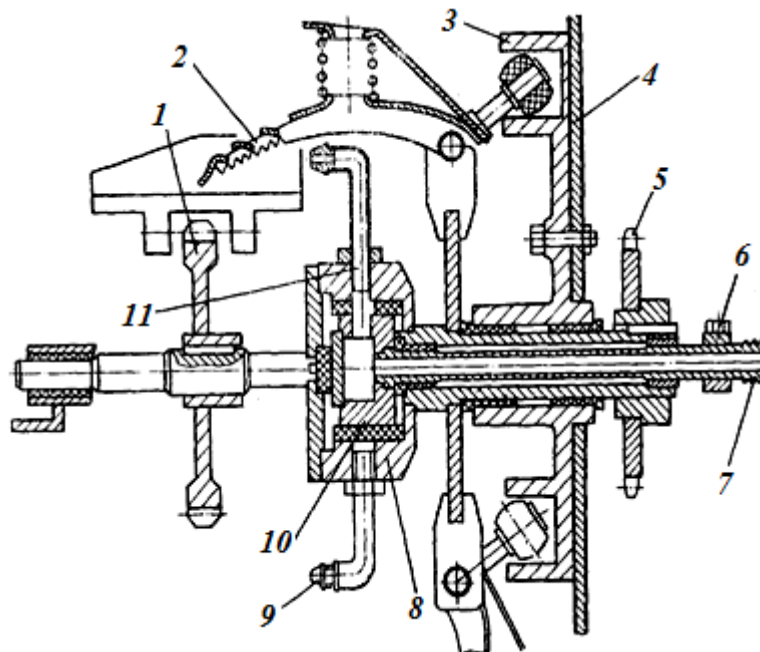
Механизм гидровымыва внутренностей
